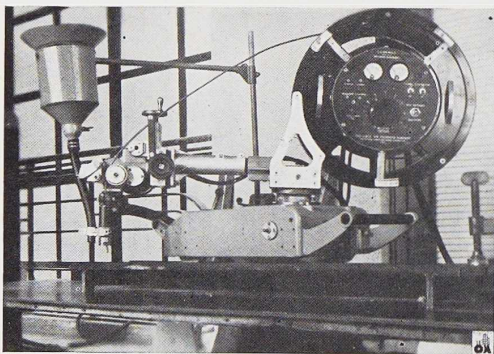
Vue d'une machine automatique de soudage sous flux.
